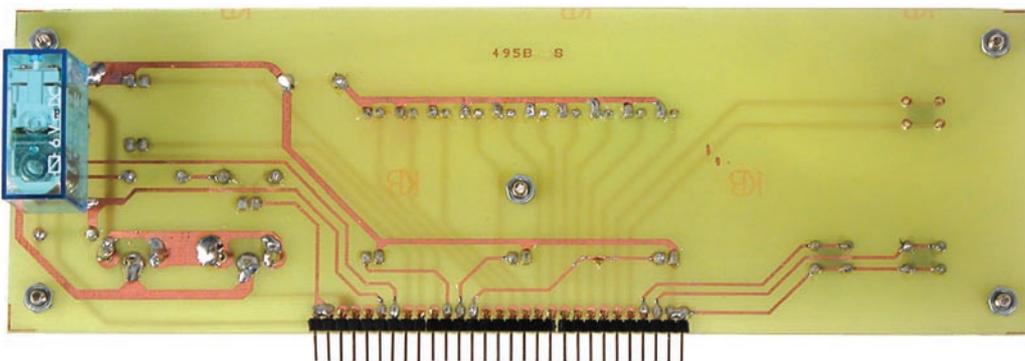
Photo d'un des prototypes de la platine interface, côté soudures.
